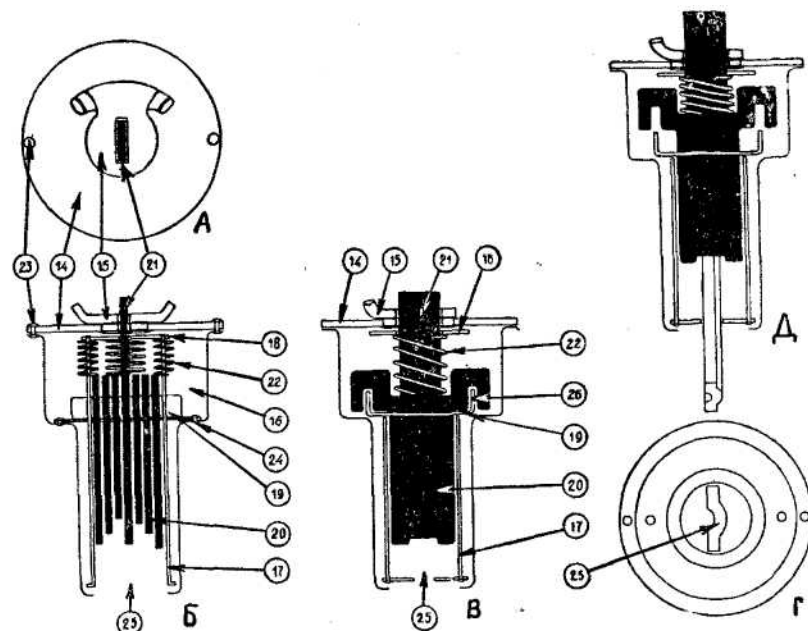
Устройство патрона прирезного цилиндрического замка с пластинками в патроне.
